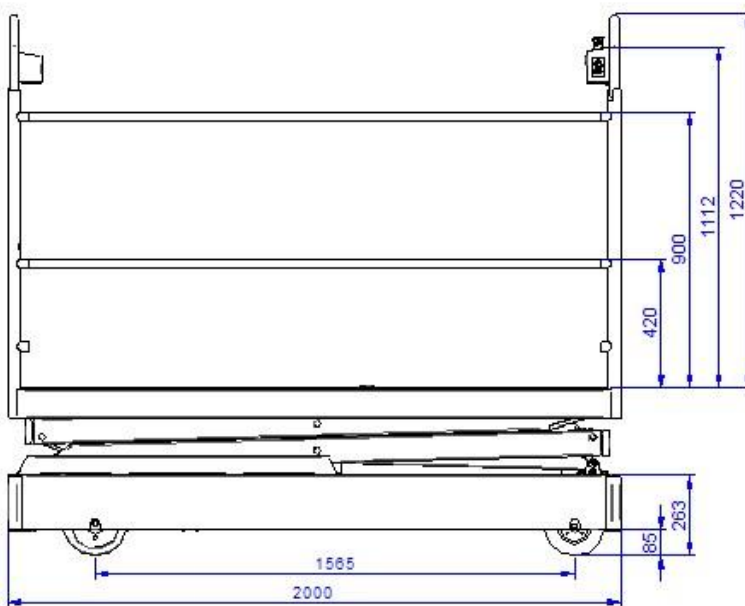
; Dimensions de la longueur en mm, 2 pantographes
